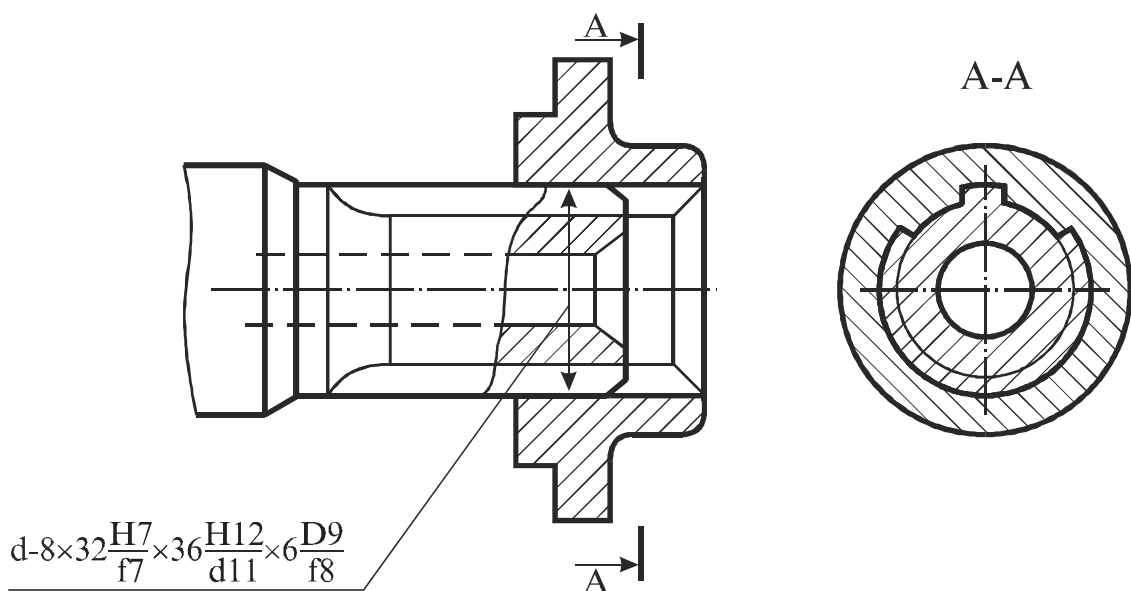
Пример оформления сборочного чертежа шлицевого соединения
